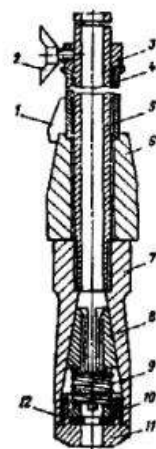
Приспособление для забивки заземлителей вручную:
